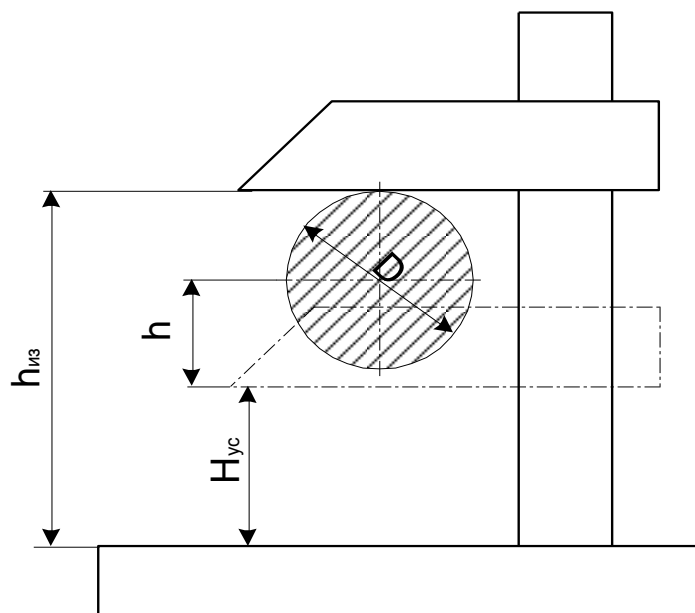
Способ установки упорки для образования заднего угла штангенрейсмусом
